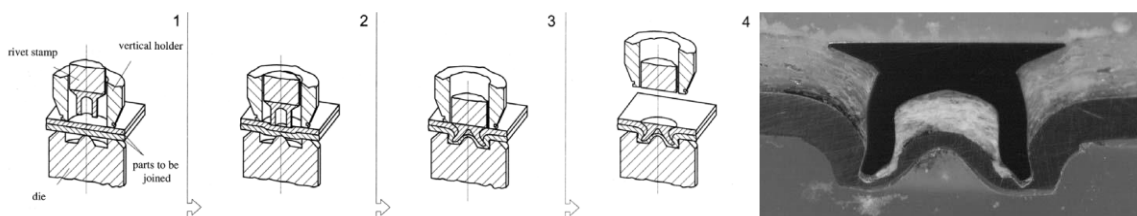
Principe du procédé de rivetage auto-poinçonneur [31] et vue coupe d'un joint riveté hybride [33]
